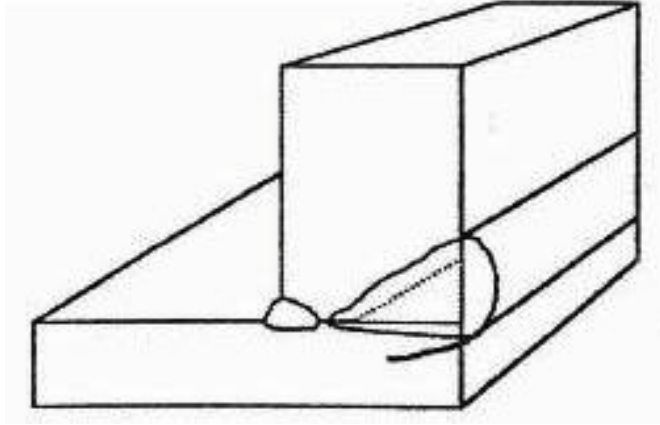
Grietas en el pie de la soldadura
